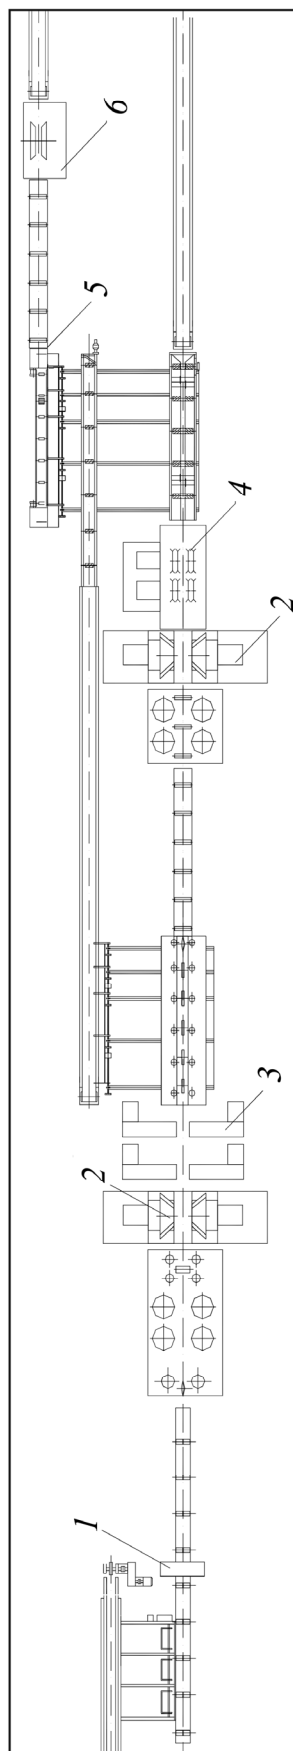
Схема расположения оборудования в цехе на базе ленточнопильных и круглопильных станков с фрезерными приставками: 1 – измерительное устройство; 2 – фрезерный модуль; 3 – спаренные ленточнопильные станки; 4 – двухвальный многопильный круглопильный станок; 5 – торцовочный станок; 6 – фрезерно-обрезной станок
